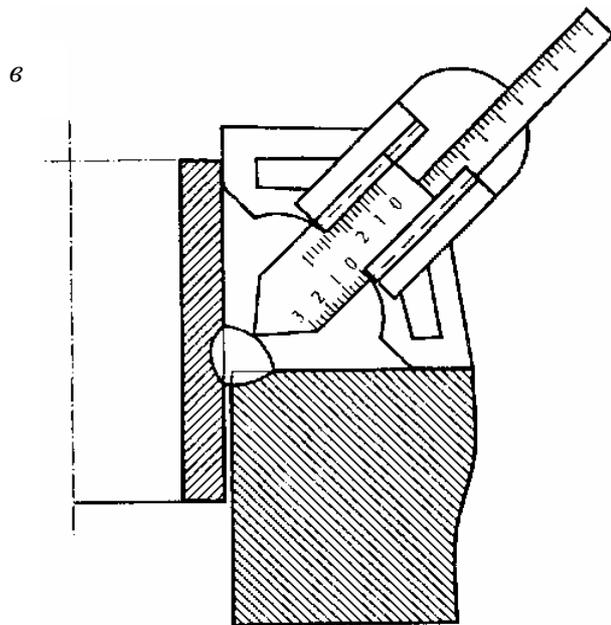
Продолжение.* Контроль сварных швов шаблоном конструкции В.Э. Ушера-Маршака: *в* – измерение высоты катета углового шва K ; *г* – измерение высоты валика усиления g и выпуклости корня шва g_1 стыкового сварного соединения
